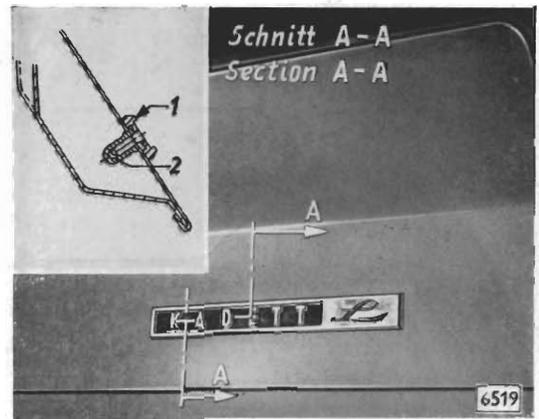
Befestigung des Schriftzuges „Kadett-L“
